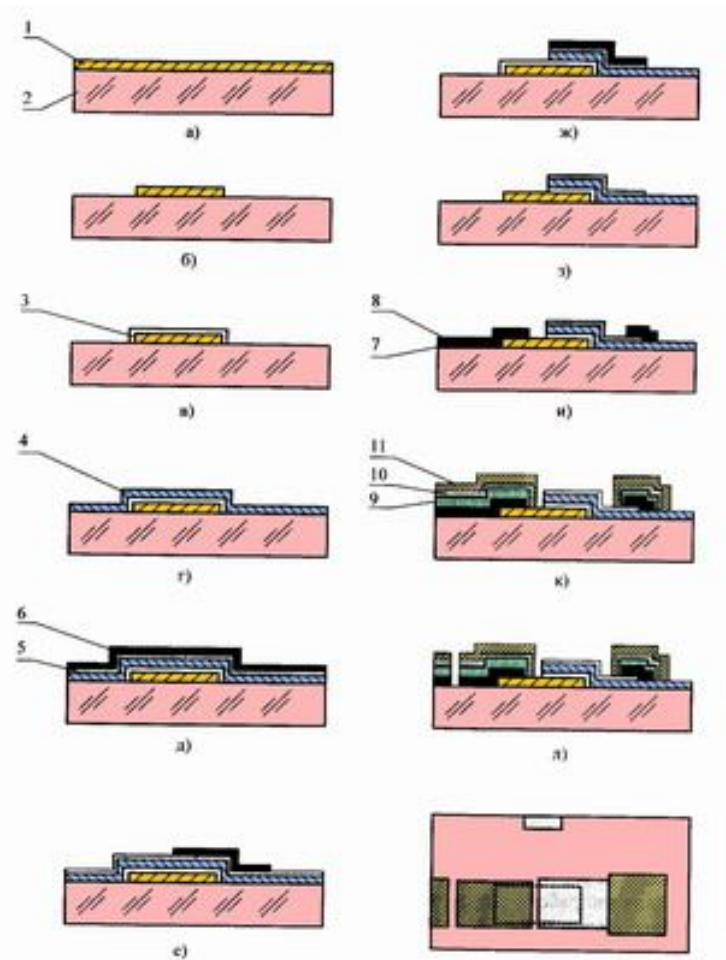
Схема изготовления МПП с тонкопленочными конденсаторами: 1 — подложка (поликор); 2 — пленка тантала Та ($h = 0,6 \text{ мкм}$); 3 — палладий Рд ($h = 0,2 \text{ мкм}$); 4 - пленка двуоксида кремния; 5 - пленка тантала Та ($p = 50 \text{ Ом/р}$); 6 — пленка меди Си ($h = 1 \text{ мкм}$); 7 — подслой хрома Сг ($p = 100 \text{ Ом/р}$); 8 - пленка меди Си ($h=1 \text{ мкм}$); 9 - гальваническая медь Си; 10 — гальванический никель Ni; 11 — гальваническое золото Au.
